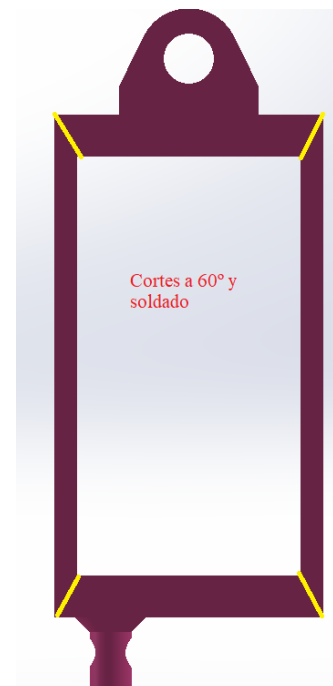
Vista de pieza N°12 (Fuente 100)
